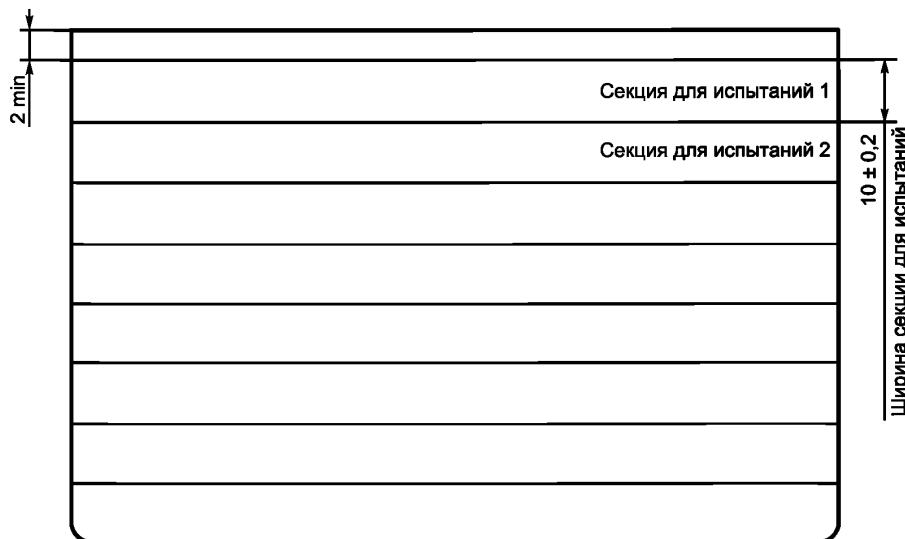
Подготовка образца к измерению прочности сцепления
